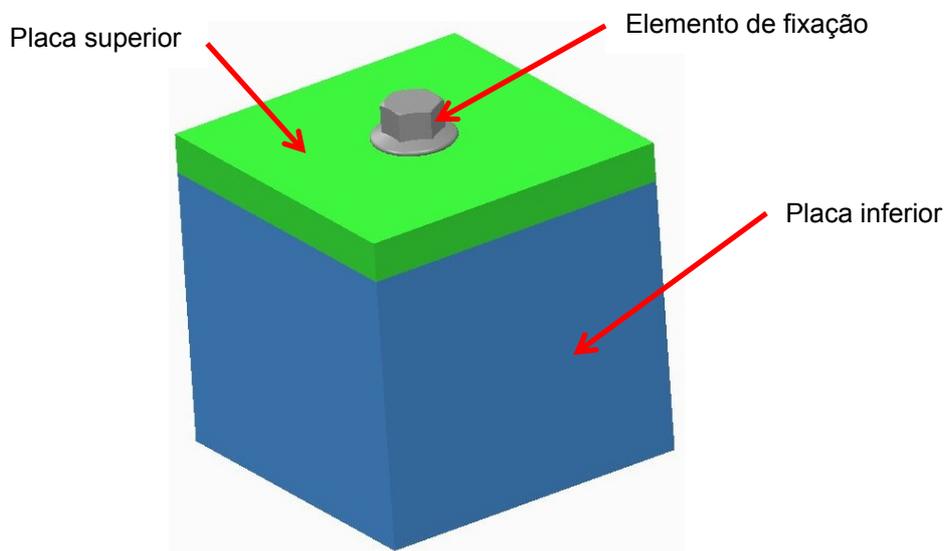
Conjunto base (placa superior + placa inferior + elemento de fixação)
